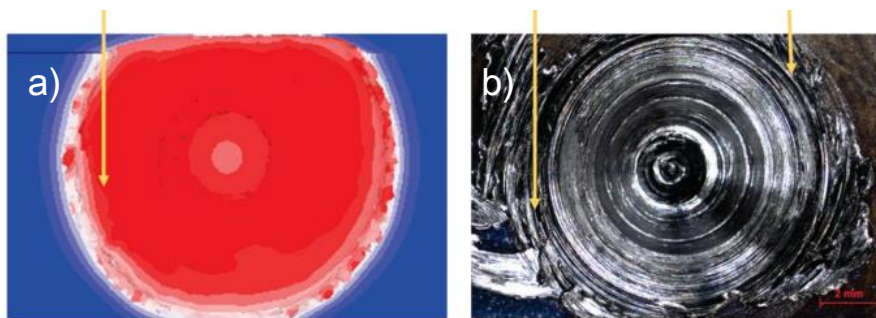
a) Modelo tridimensional del punto de soldadura, b) Imagen del punto de soldadura generado mediante el proceso FSSW.
